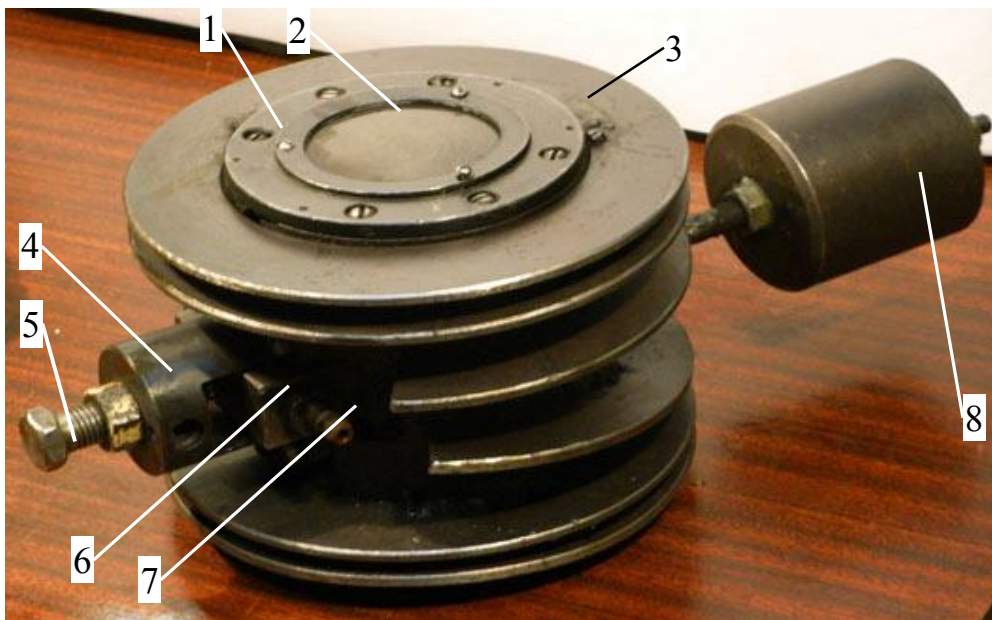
Подшипниковый узел в сборе (фото): 1 – корпус, 2 – крышка, 3 – диск радиатора охлаждения, 4 – кронштейн, 5 – винт нагрузочный, 6 – башмак, 7 – штуцер, 8 – груз
